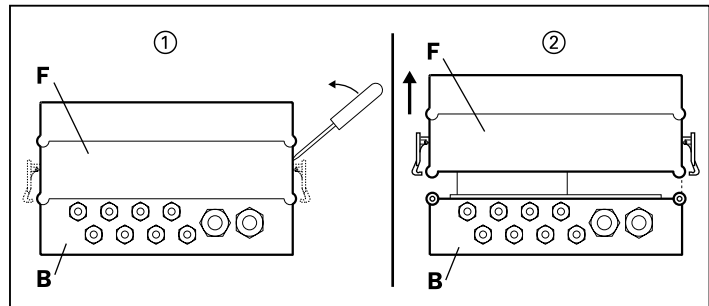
IP-65-Gehäuse, Gehäusefrontteil abnehmen
